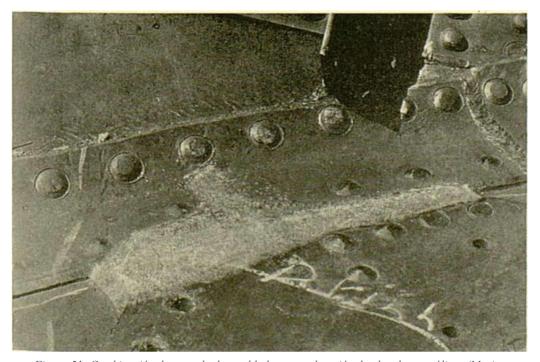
Combinación de remachado y soldadura para la unión de planchas metálicas (Marine Engineering & Shipping Age)
